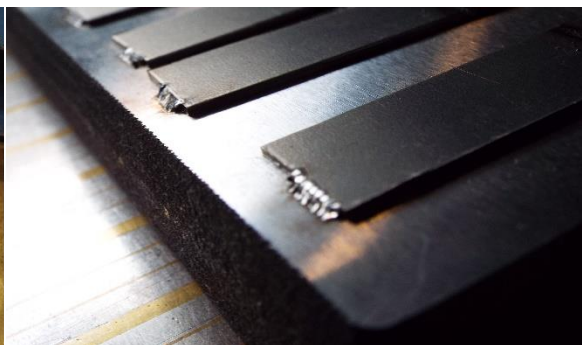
Soldadura das extremidades das amostras à base fixadora
